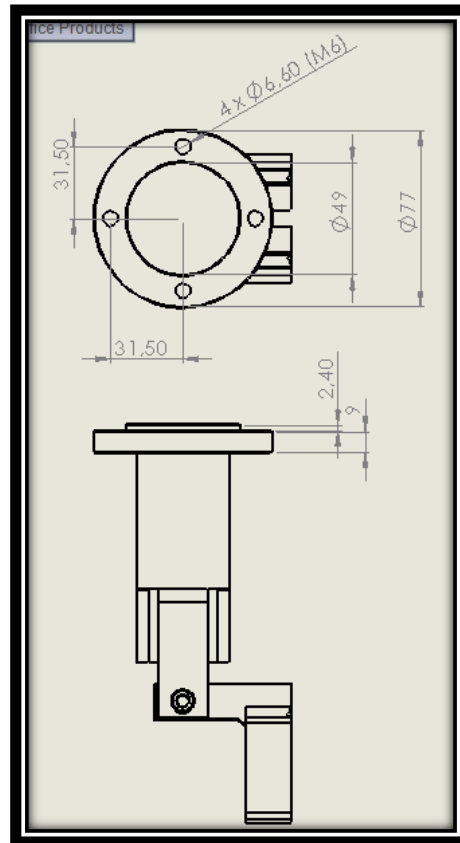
Desenho cotado da flange de saída da garra da Bosch
